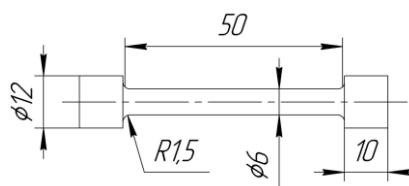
Внешний вид и размеры образца выращенного для испытания на растяжение
